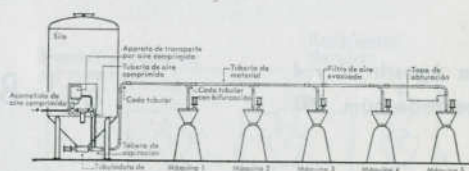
Equipo de transporte por aire comprimido, para alimentar un grupo de máquinas con un mismo tipo de material. El aparato de transporte aspira el material granulado del silo, a través de la boca de aspiración, pudiendo regularse el caudal de aire. El material granulado se inyecta a la tolva de la máquina 1, hasta que el nivel de material alcance el borde inferior del tubo de transporte, que penetra en el interior de la tolva. A continuación se llenan consecutivamente de la misma forma las tolvas de las máquinas 2 a 5. Después que se hayan llenado todas las tolvas se desconecta el aire comprimido por medio de un equipo de mando automático. Una vez transcurrido un tiempo fijado previamente, vuelve a conectarse automáticamente la instalación de transporte, volviendo a completar el material granulado en las tolvas de las máquinas transformadoras tal como se ha comentado.
